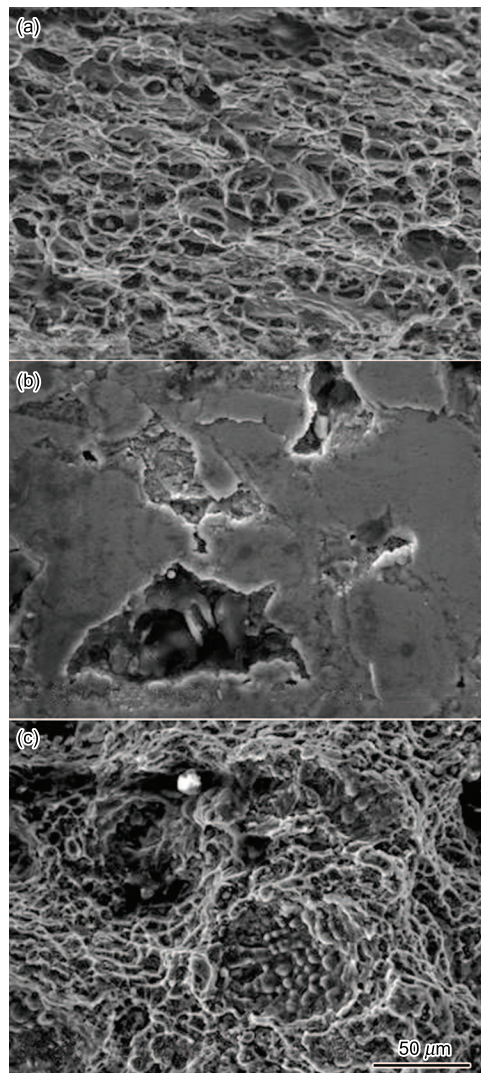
P-MIG 电弧熔 - 钎焊接头拉伸断口形貌
